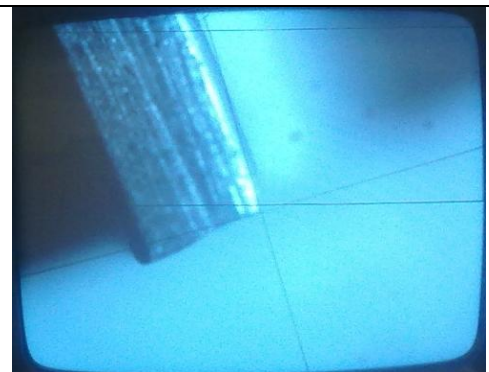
Cordão de soldadura do provete 6
